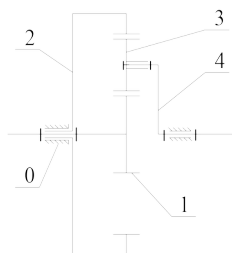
Рядовой ступенчатый зубчатый механизм
